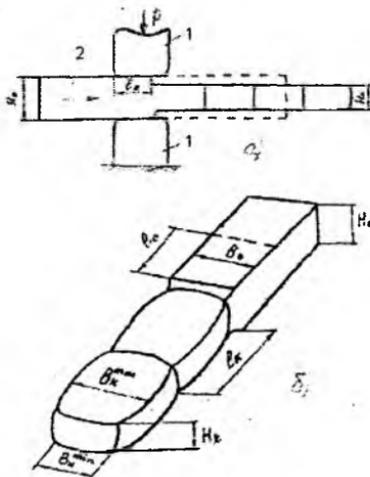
Схема протяжки. 1- бойки, 2 – заготовка
